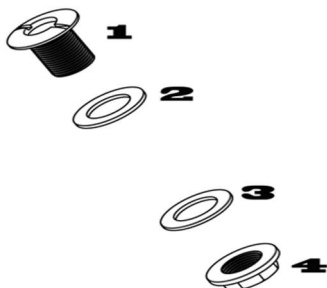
Втулка или резьбовая пробка (стеклянная шайба находится между уплотнительным кольцом 3 и резиновым кольцом 2)
